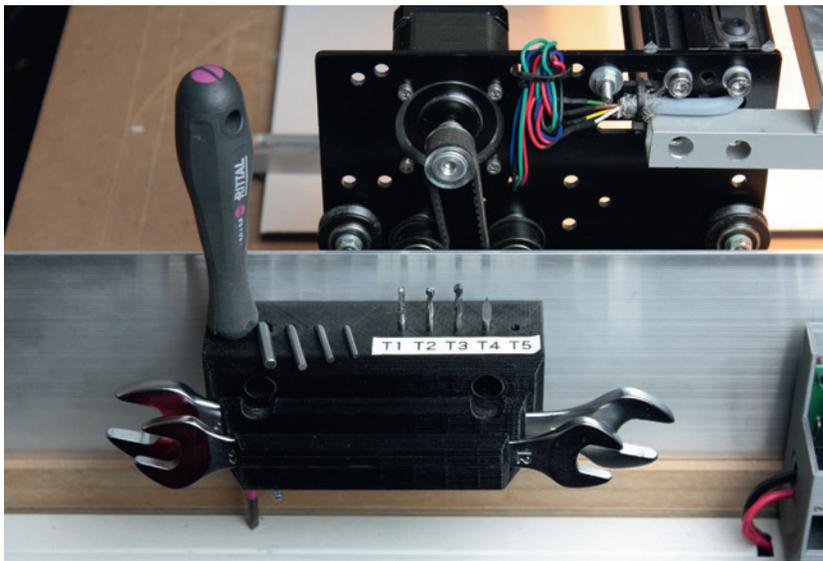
Die Fräswerkzeuge können in meinem Werkzeughalter vorsortiert nach Werkzeugnummer eingeordnet werden.
